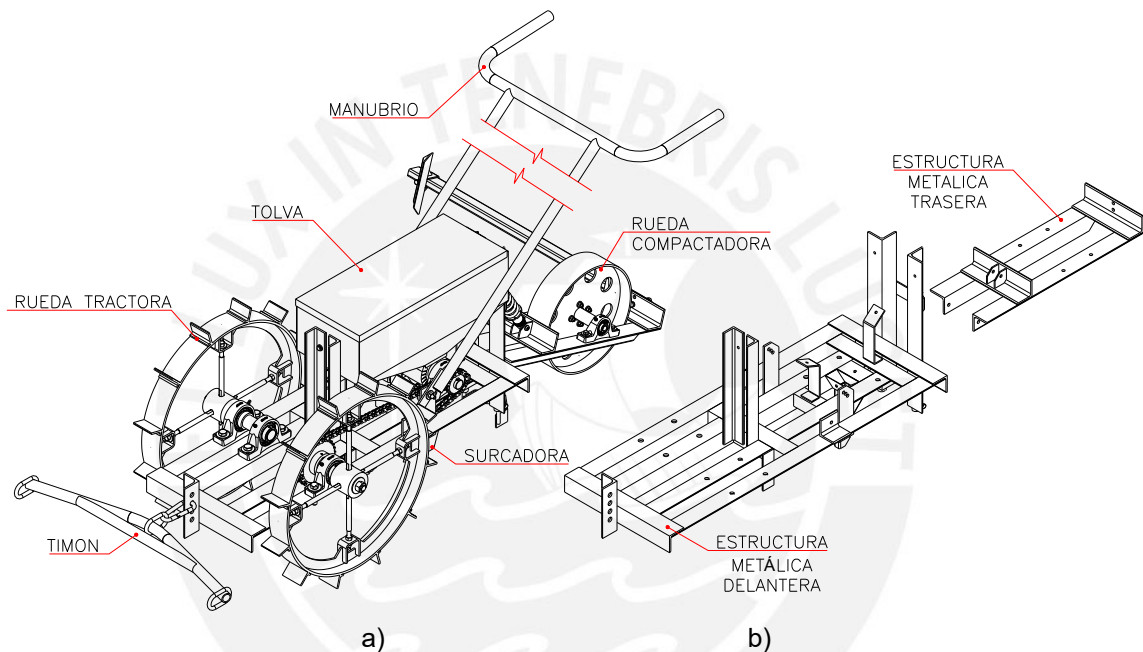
Máquina sembradora: a) Ensamble b) Estructura metálica
